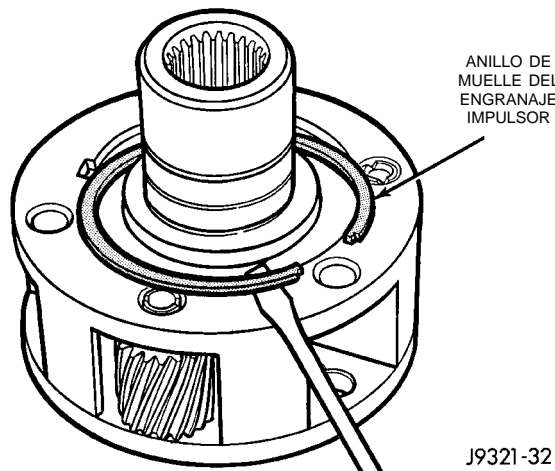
Desmontaje del anillo de muelle del engranaje impulsor
